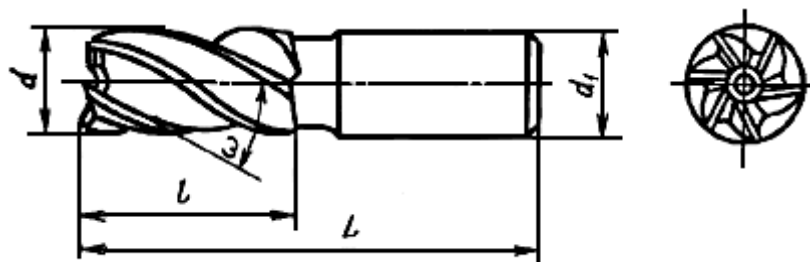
кінцева фреза з циліндричним хвостиком 2220-0019 ГОСТ 17025-71
